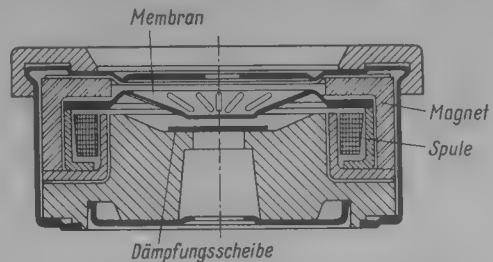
Schnittbild einer magnetischen Hörkapsel (Siemens).
